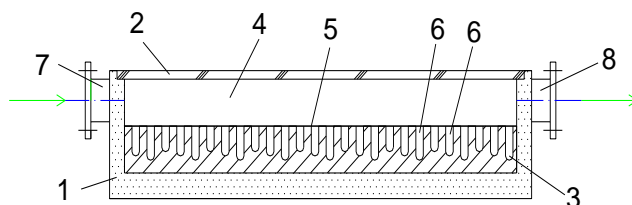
Колектор з капілярним абсорбером: 1-корпус; 2-світлопрозоре покриття; 3-капілярна структура; 4-вільний простір; 5-поверхня абсорбера; 6-поверхня абсорбера; 7,8-вхідний та вихідний патрубок
